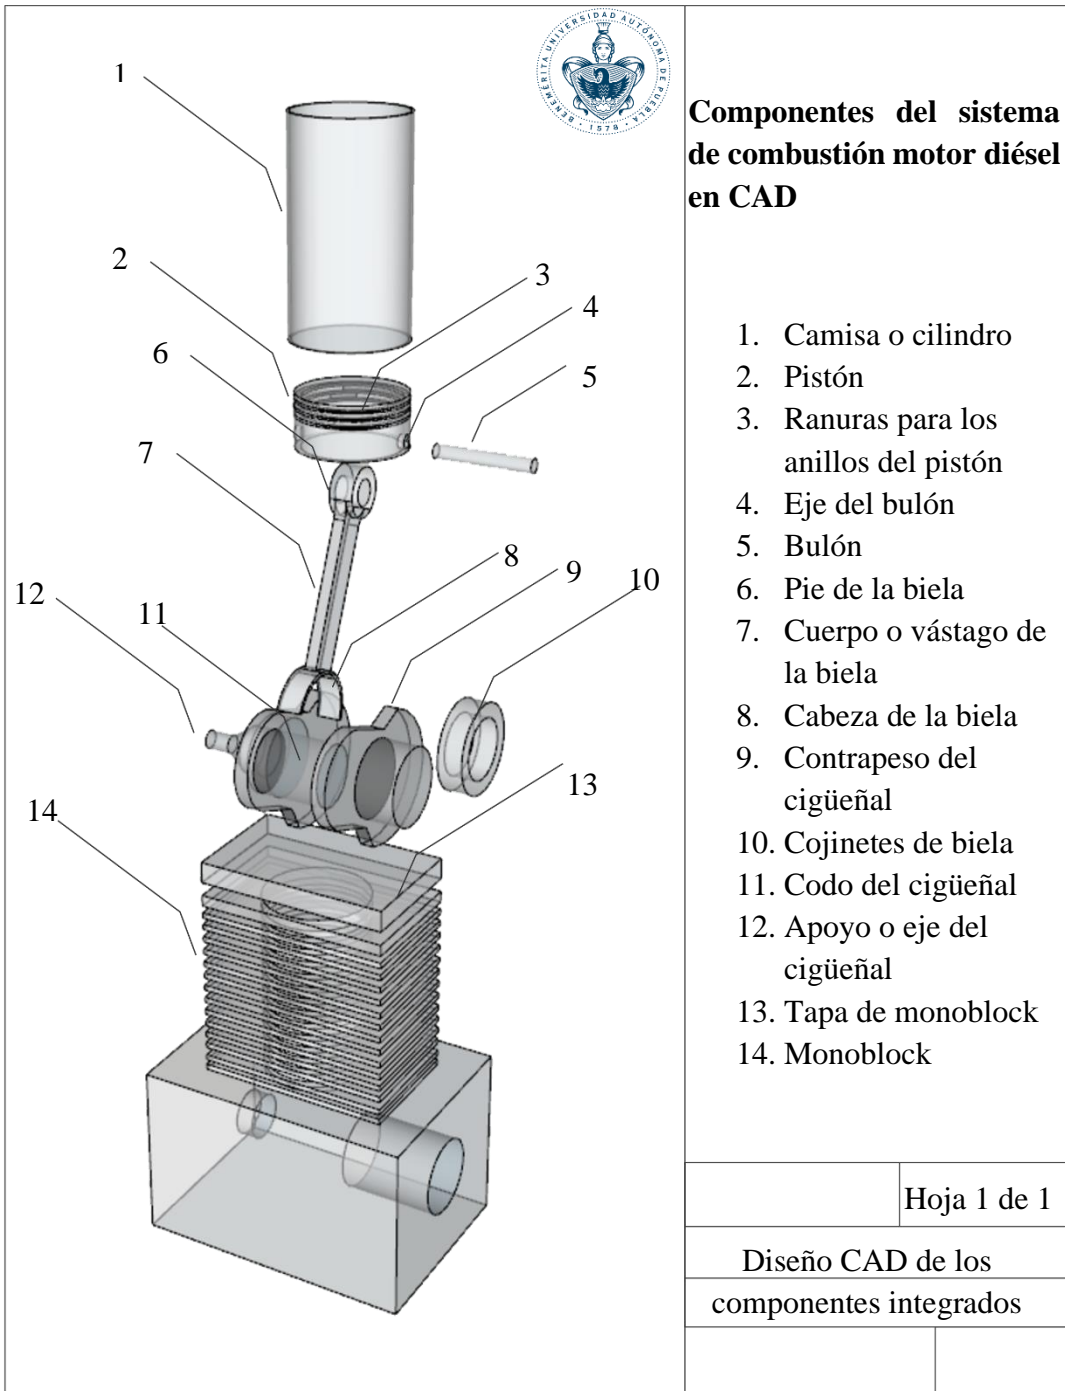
Componentes del sistema de combustión motor diésel en CAD.
